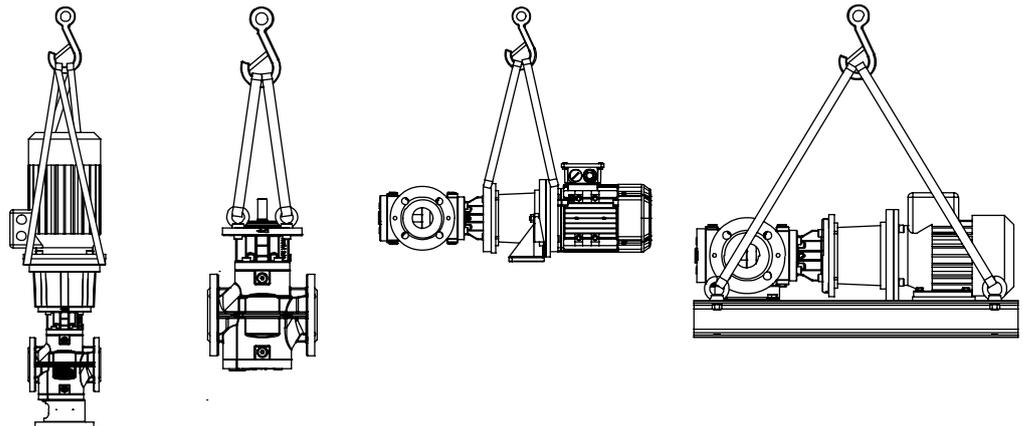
Befestigung Hebezeug - Prinzipbilder
